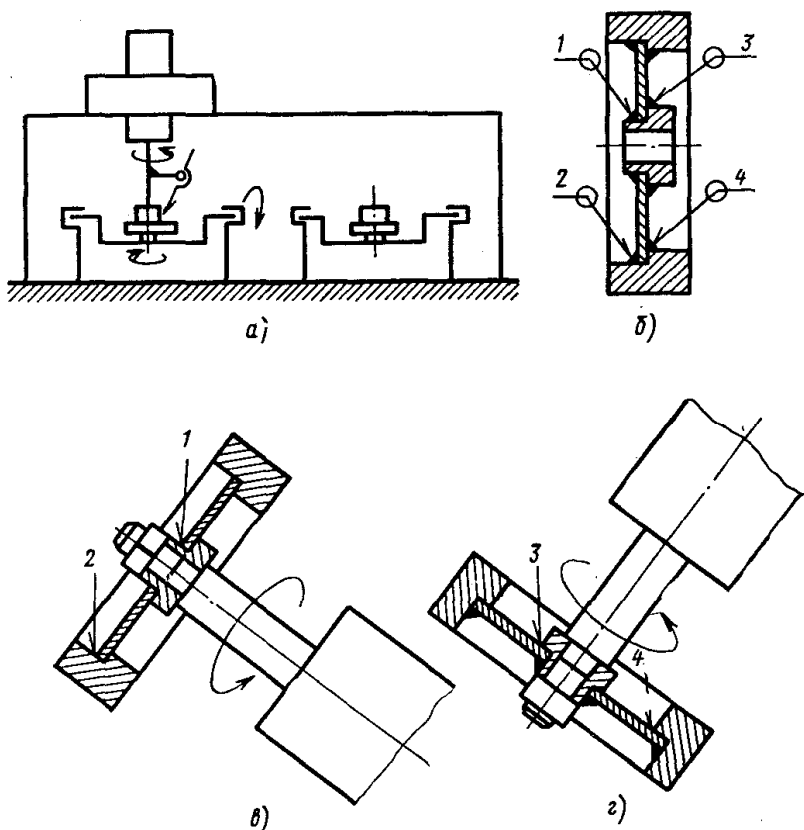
РТК для сварки шестерен большого размера:
